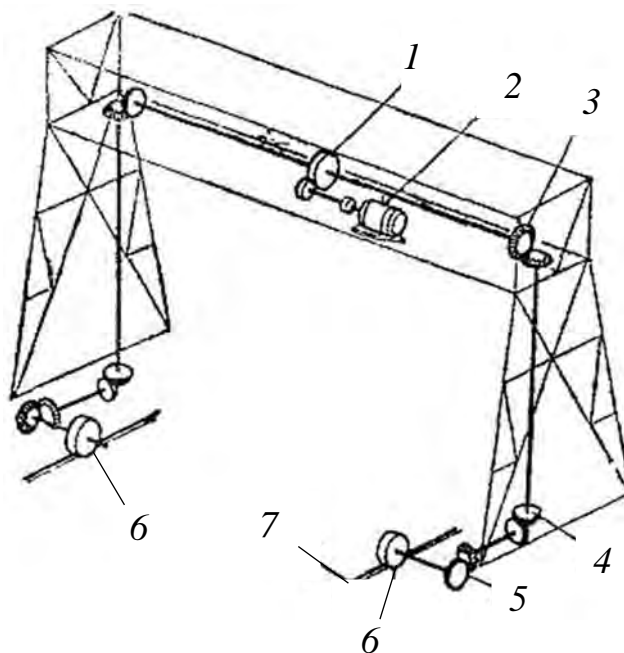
Механизм передвижения козлового крана при установке одного двигателя на мосту: 1 – редуктор; 2 – двигатель; 3–5 – конические редукторы; 6 – ходовые колеса; 7 – рельсы
